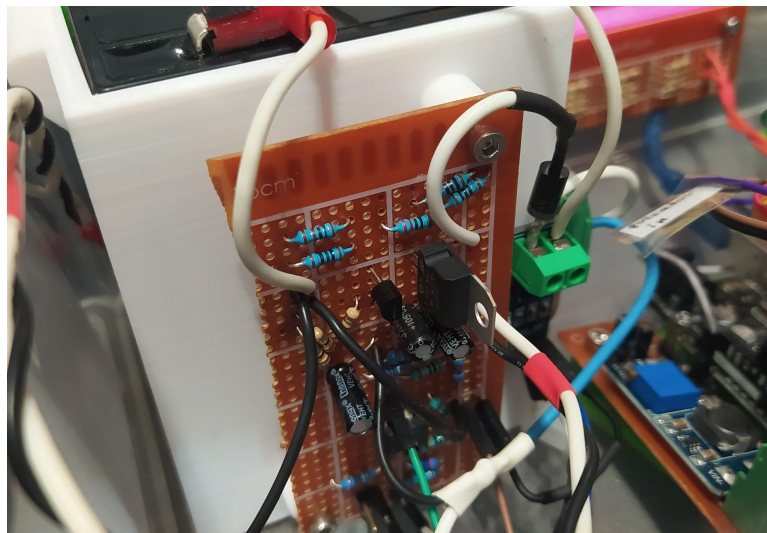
Imagen del CLC instalado en la caja de electrónica [fuente: elaboración propia]
